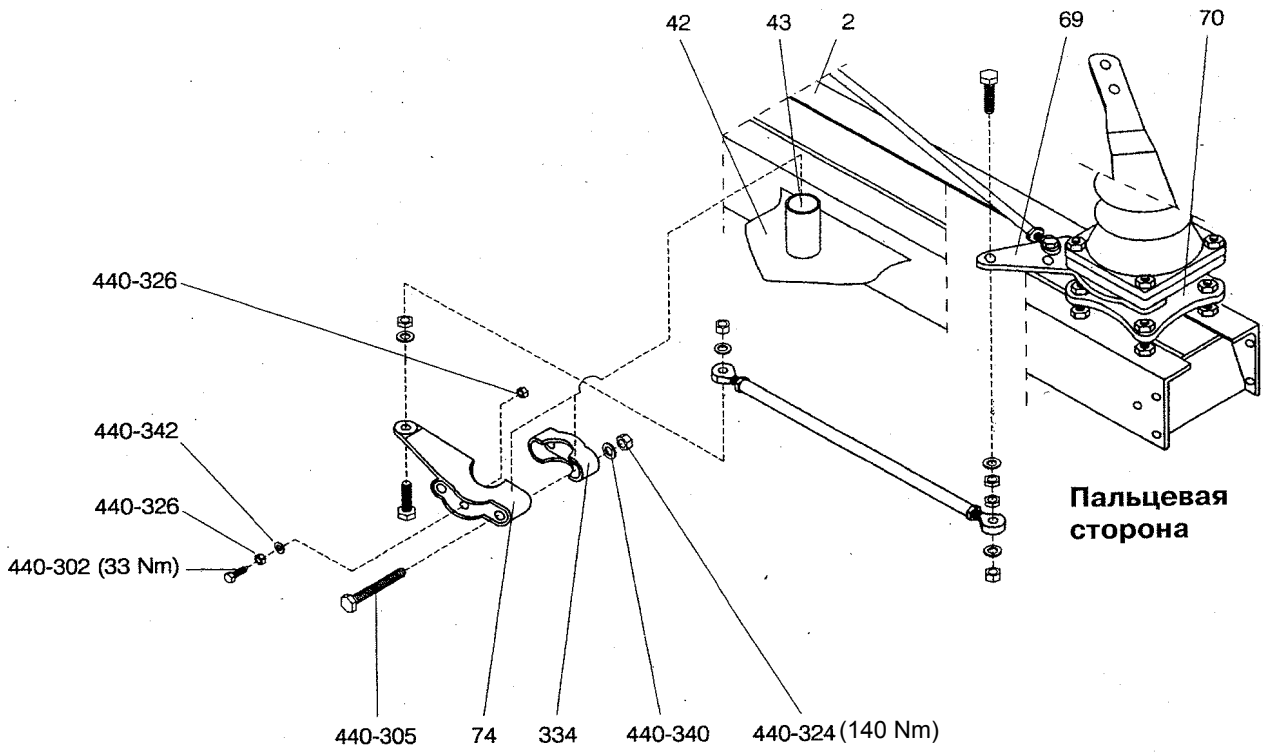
Установка приводного механизма разъединителя; раздельная установка. Установка приводного рычага (74) при расположении приводного механизма на стороне открывания
